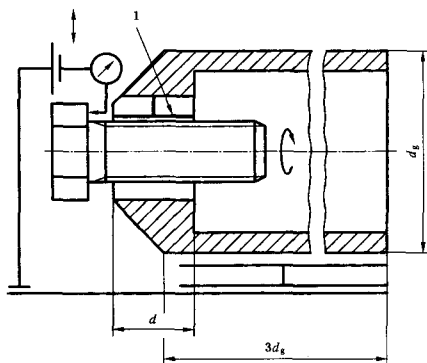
用于检验图 56 中规定的全跳动公差的测量装置
